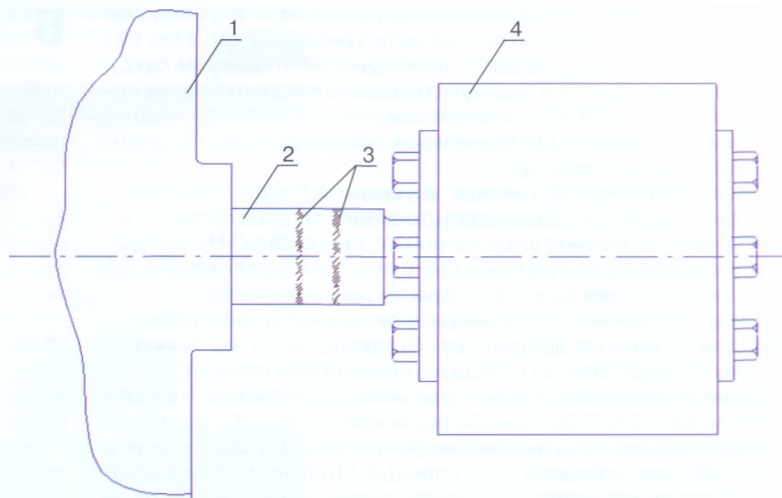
Положение деталей колесной пары после двукратного сдвига диска колеса:
